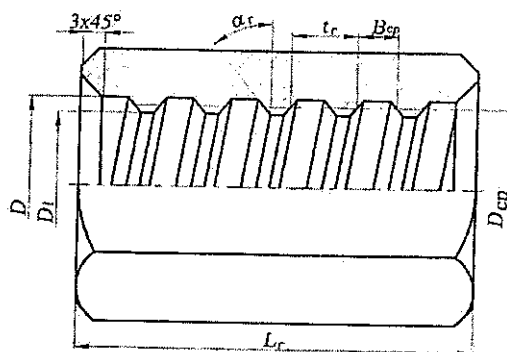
Гайка для контроля арматурного проката винтового профиля
